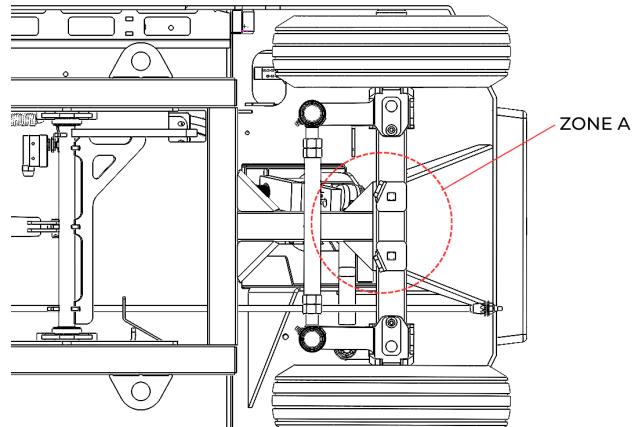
Zone A (soudures et tube d'essieu).
